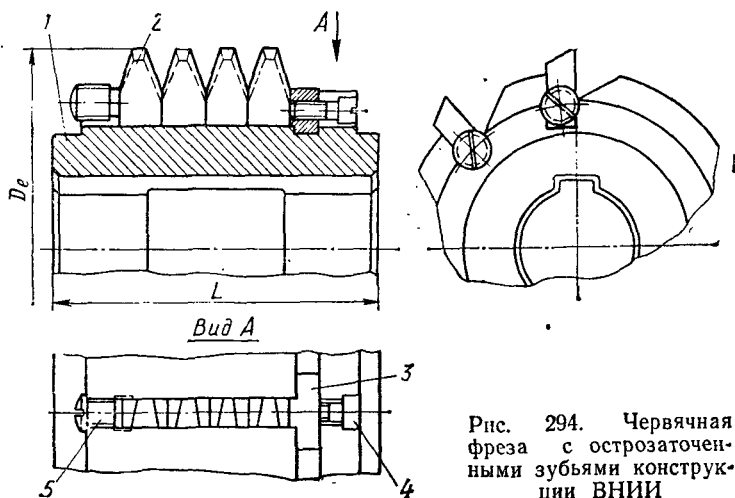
Червячная фреза с острозаточенными зубьями конструкции ВНИИ
